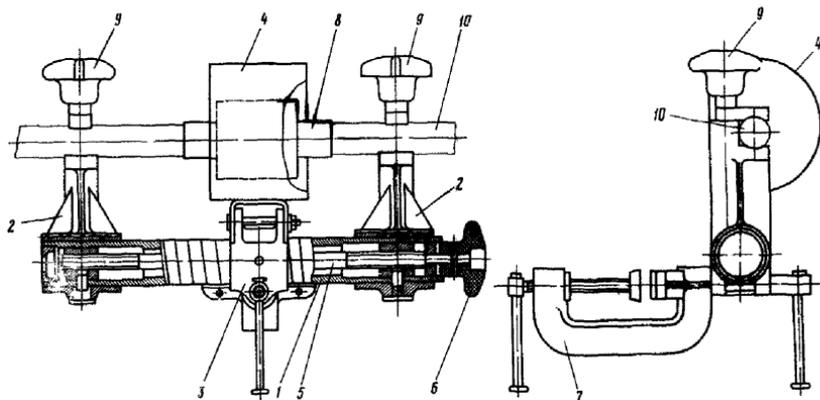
Приспособление для сварки проводов с помощью термитных патронов типа ПГСП:
